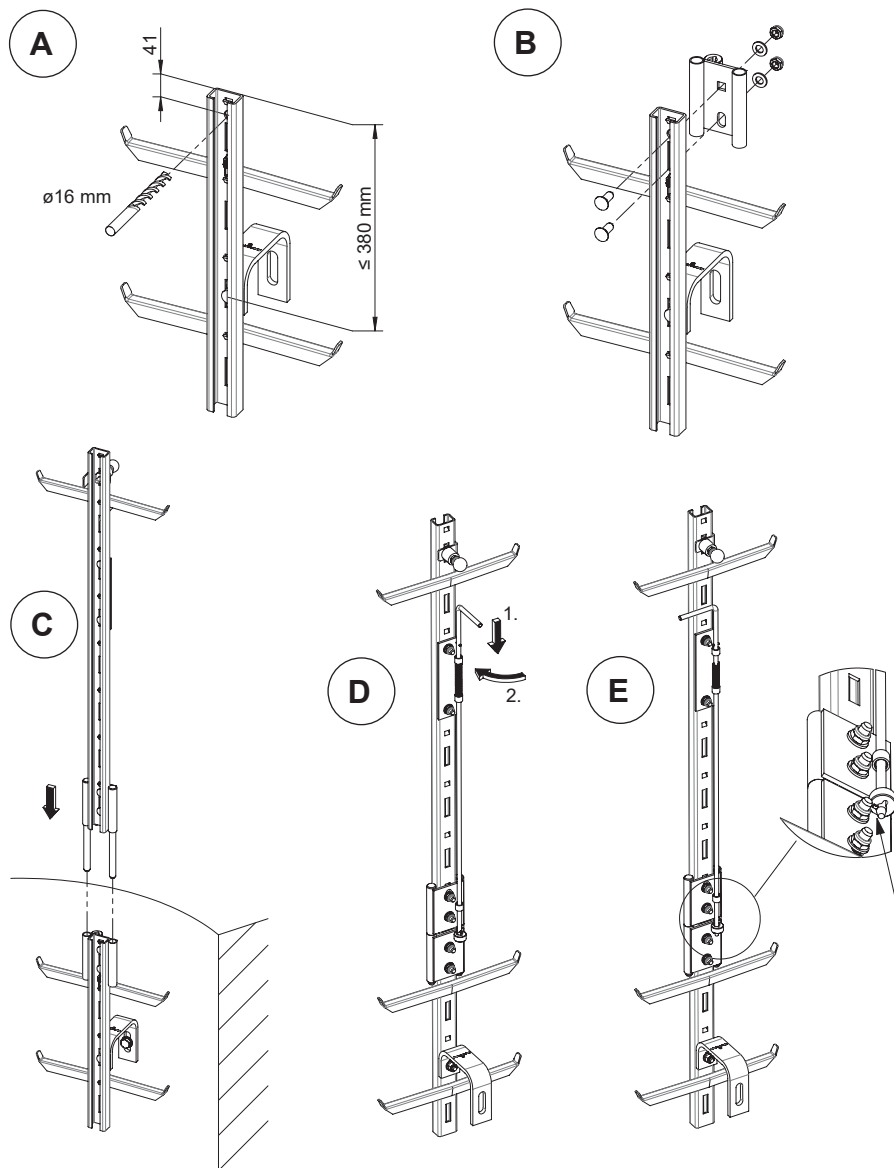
Montering aksel inn i enheten: A: Drilling og dimensjoner
